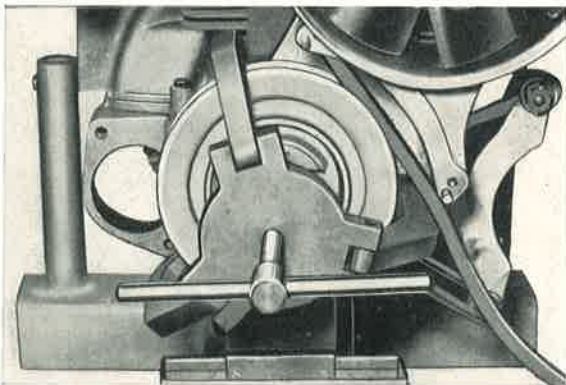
Beim ausgebauten Motor kann die Riemenscheibe mit einem Universal-Abzieher abgezogen werden.
